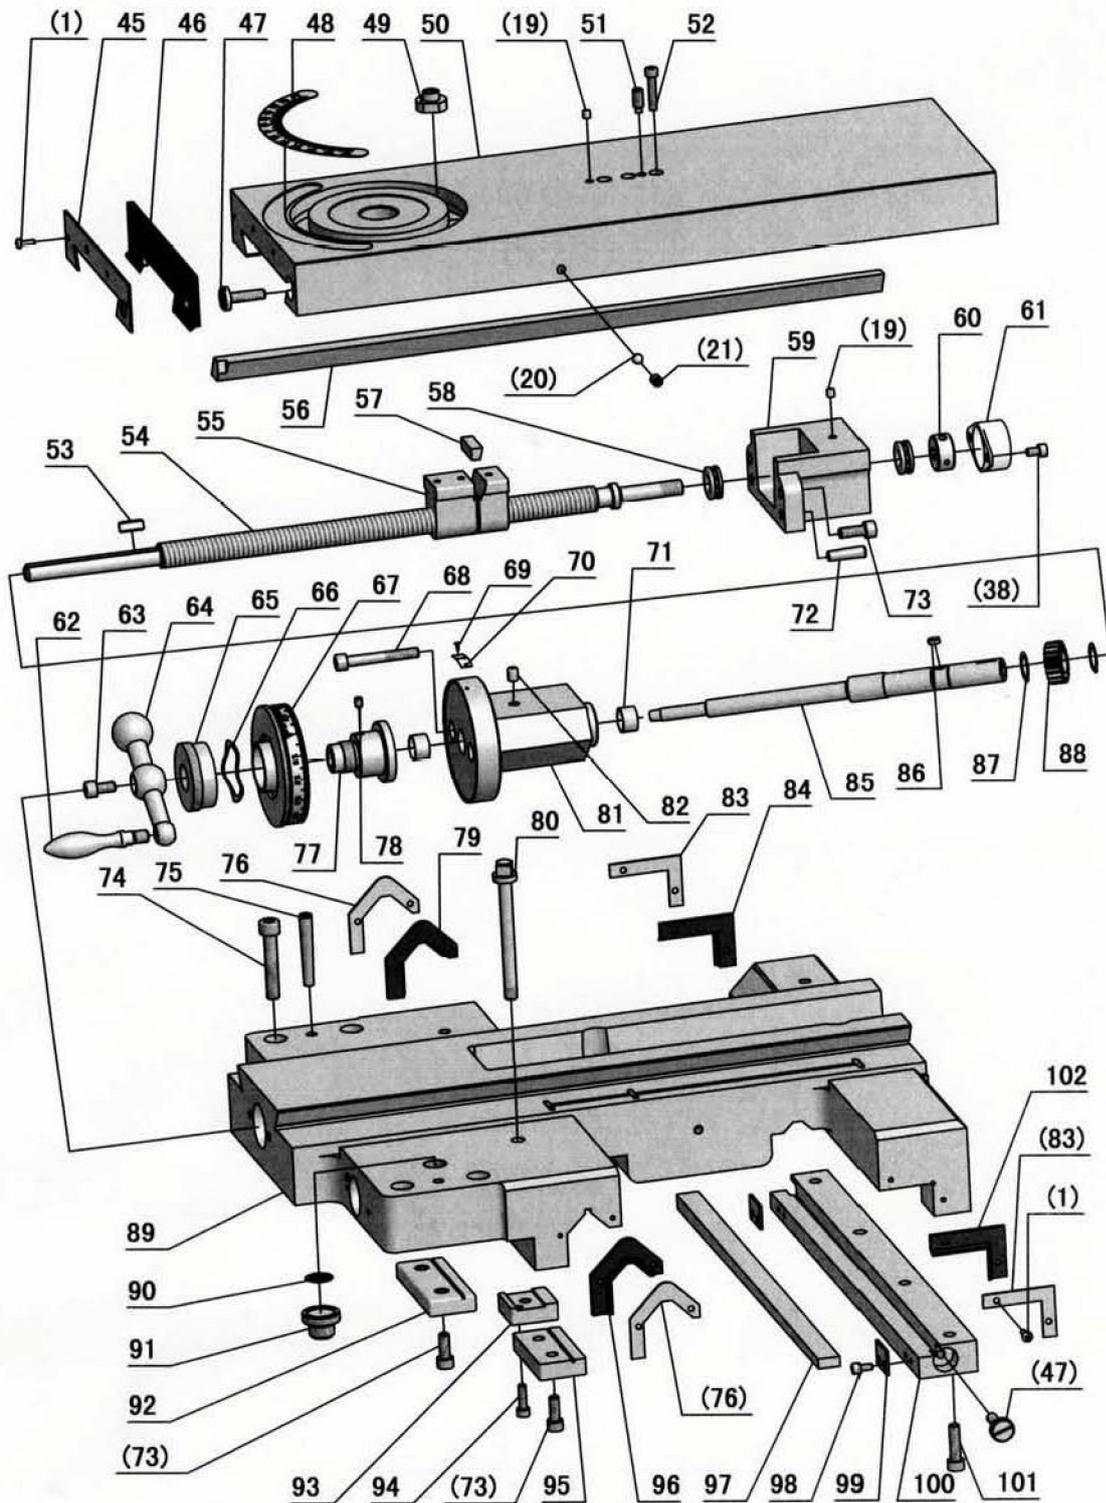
Planschlitten 1 von 2 –Carro transversal 1 de 2
